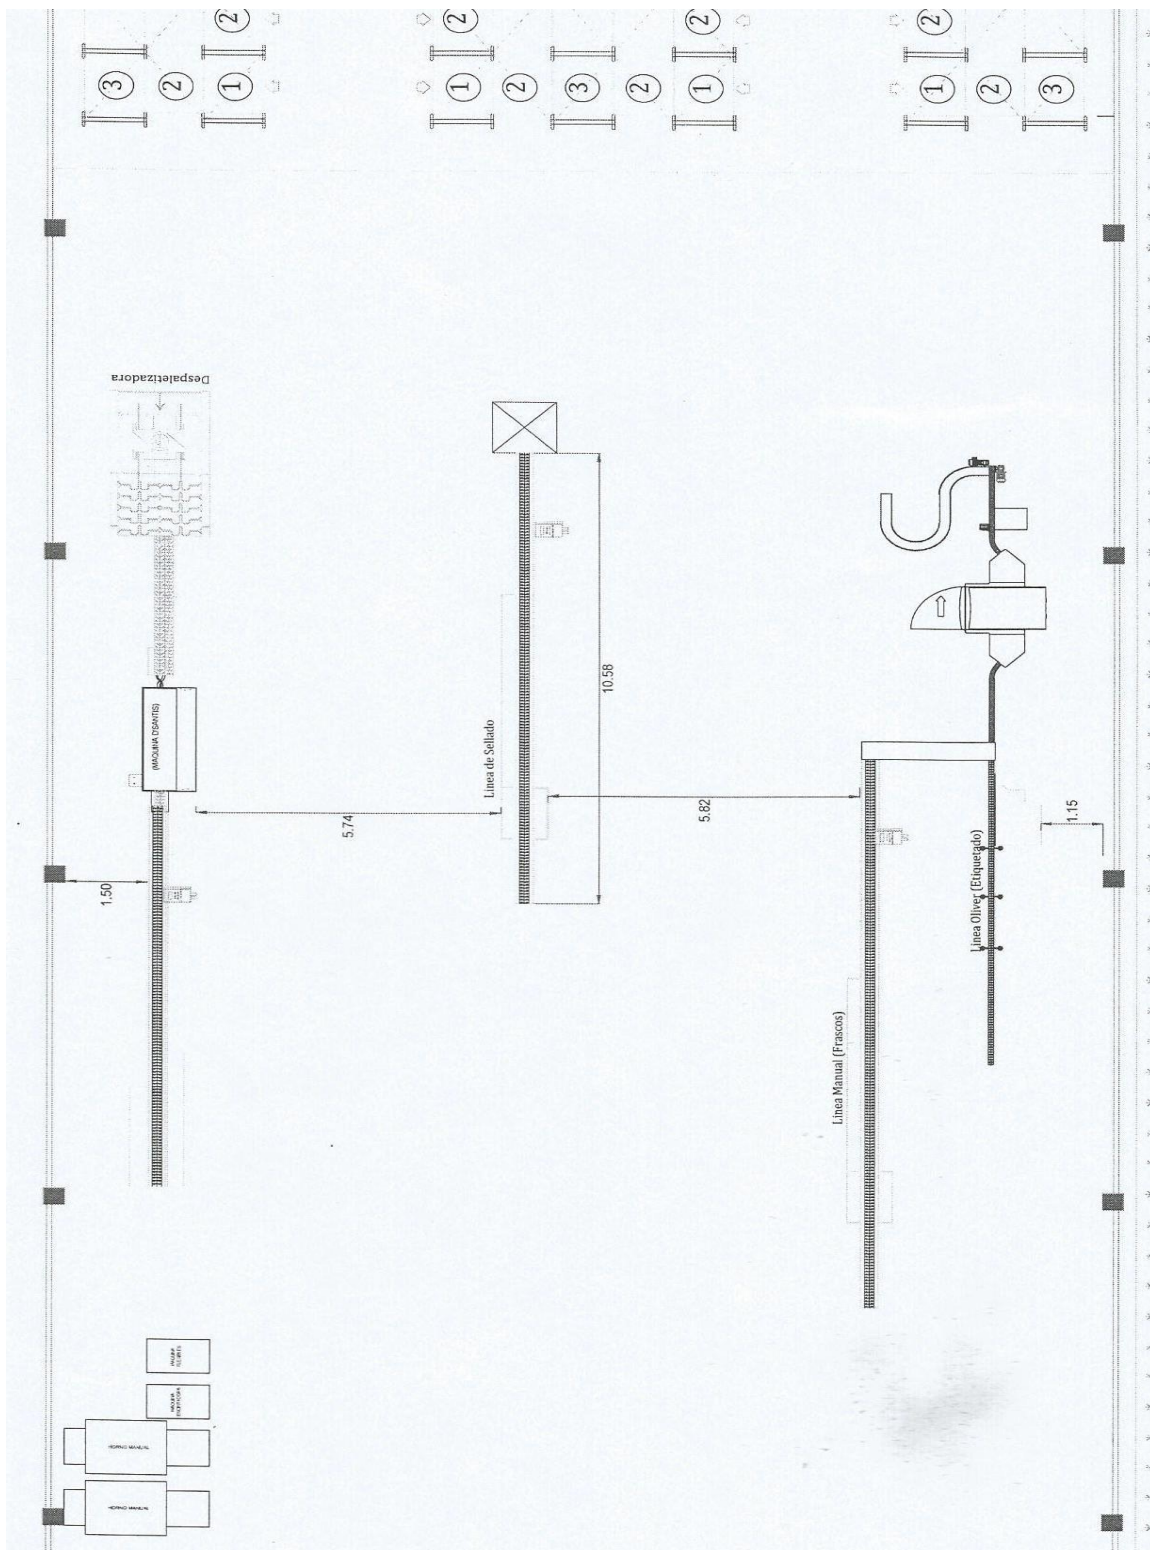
Layout del Área de etiquetado–VIRU Planta Chincha
